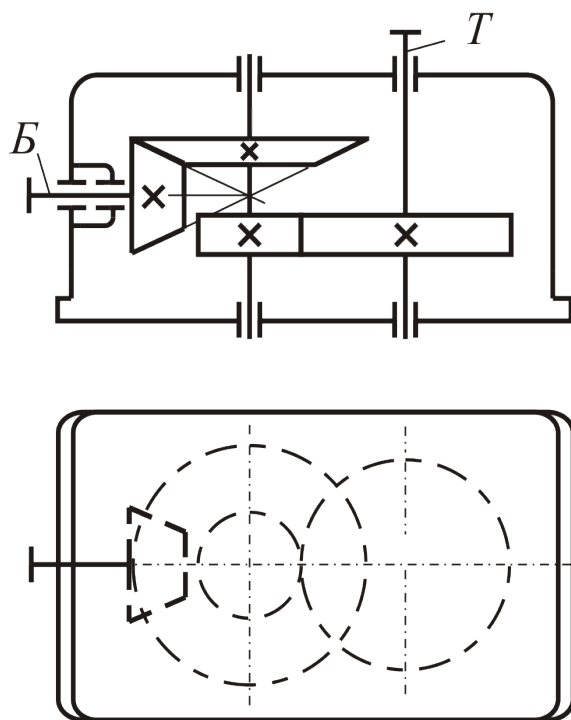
Кинематическая схема двухступенчатого коническо-цилиндрического редуктора с вертикальным тихоходным валом
